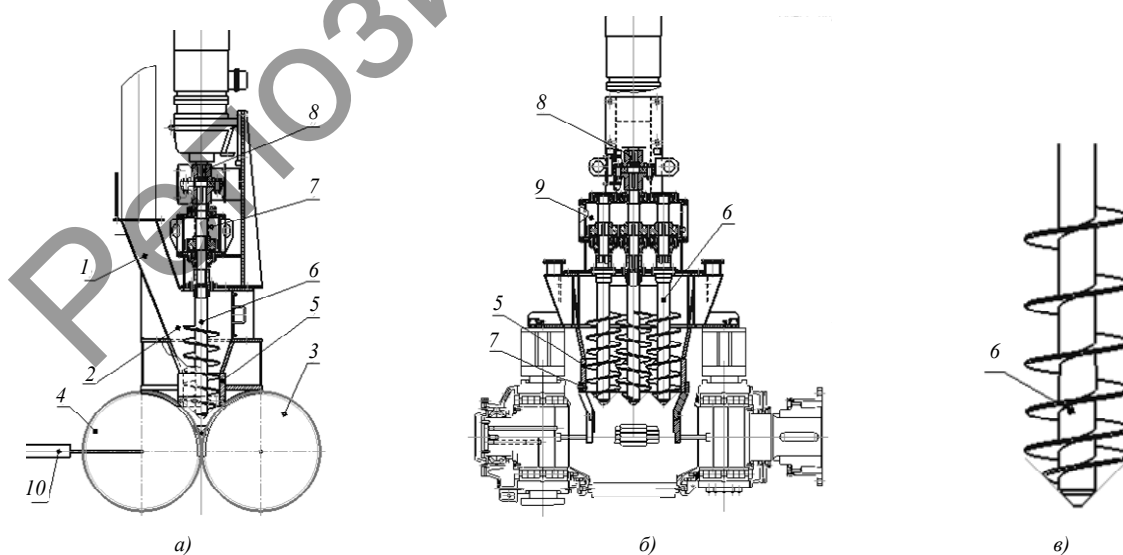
Схема валкового пресса: общий вид (*а*), вид сбоку (*б*) и шнек с переменным шагом винтовой наливки (*в*)
